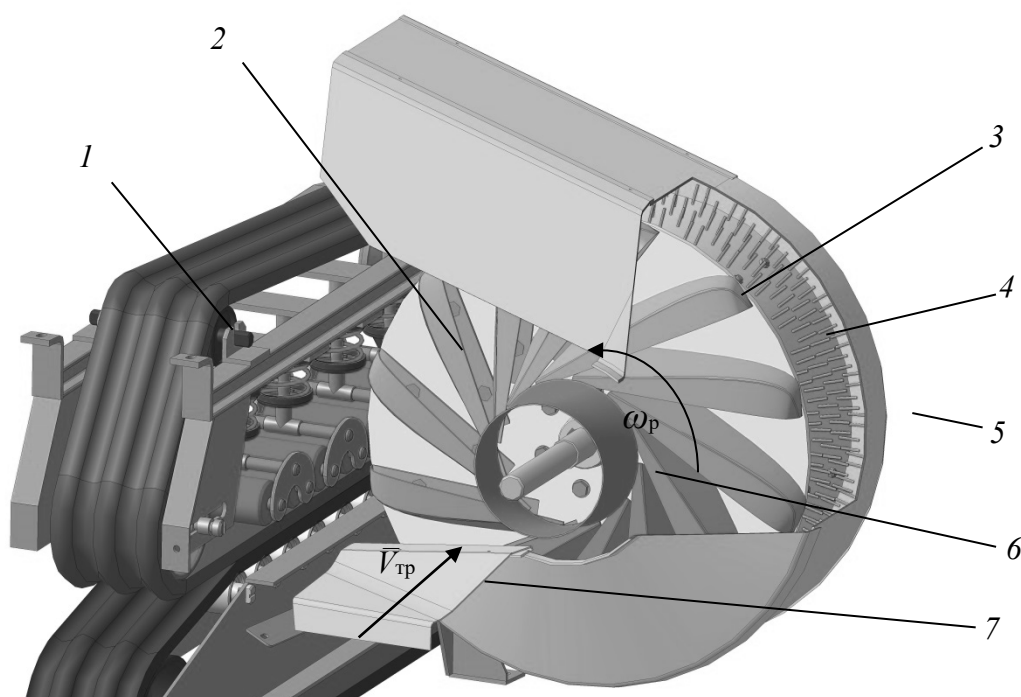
Общий вид роторного бильно-вычесывающего устройства: 1 – зажимной транспортер; 2 – ротор; 3 – бичи; 4 – вычесывающе-транспортирующая щетка; 5 – кожух; 6 – кольцо; 7 – стол.
